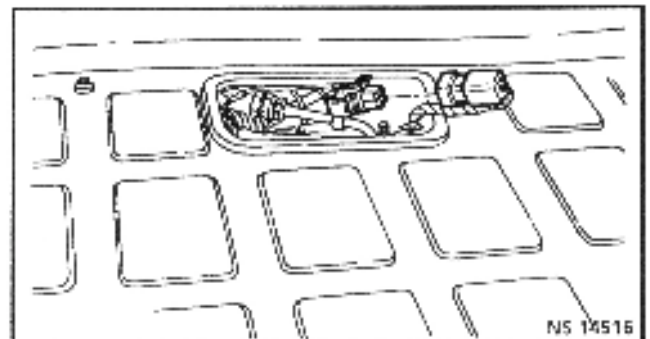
Steckverbindung - Kraftstoffpumpe
